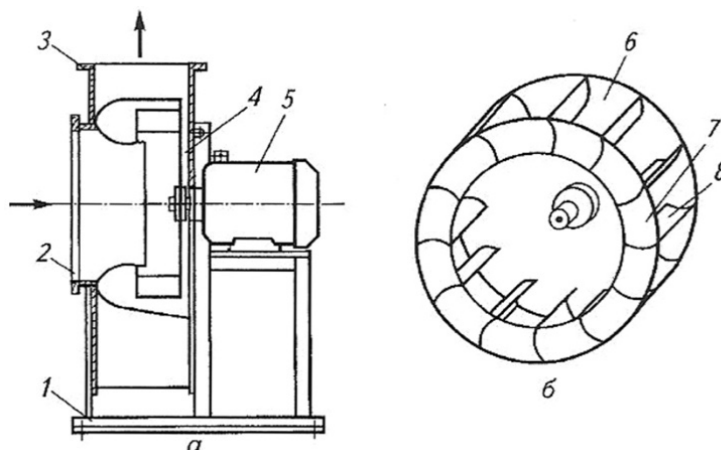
Воздушный центробежный вентилятор низкого давления:
